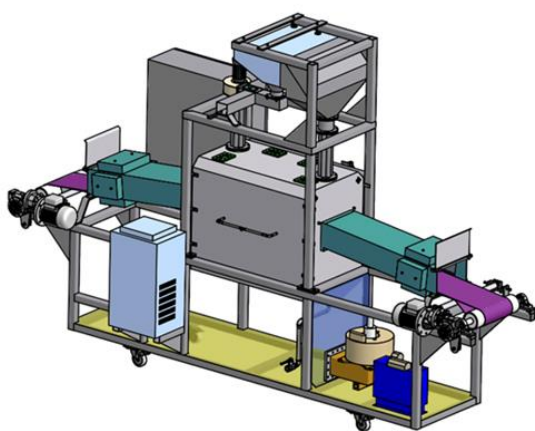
Equipo microondas situado en la Planta Piloto de Ctic Cita.
